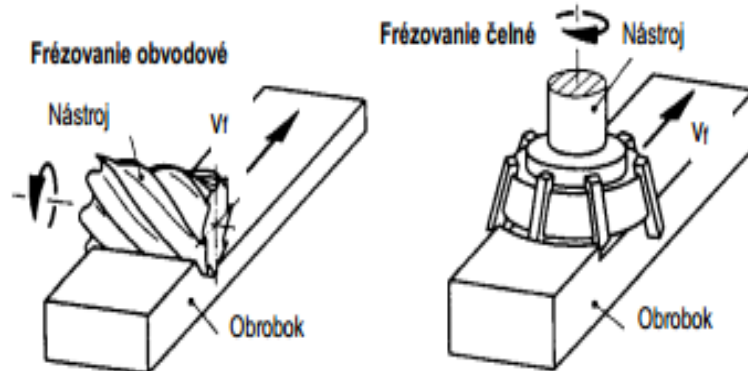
Frézovanie čelnou valcovou frézou[3]
